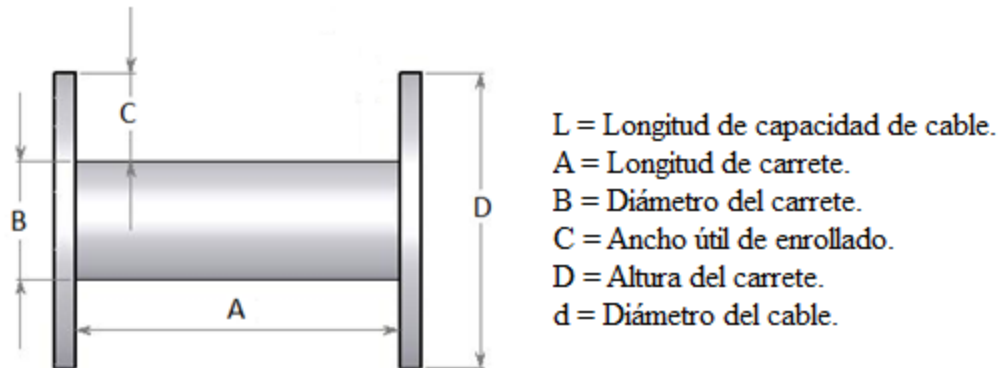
Parámetros dimensionales del carrete para cálculo de capacidad de longitud de cable.
